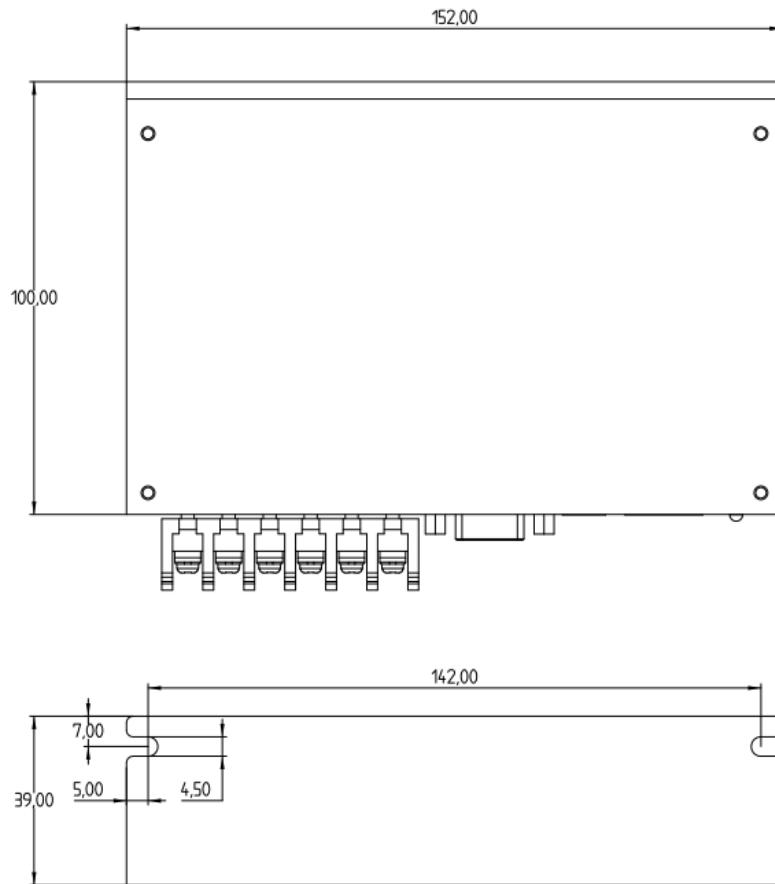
DS/RS10270E 安装尺寸图 (mm)
